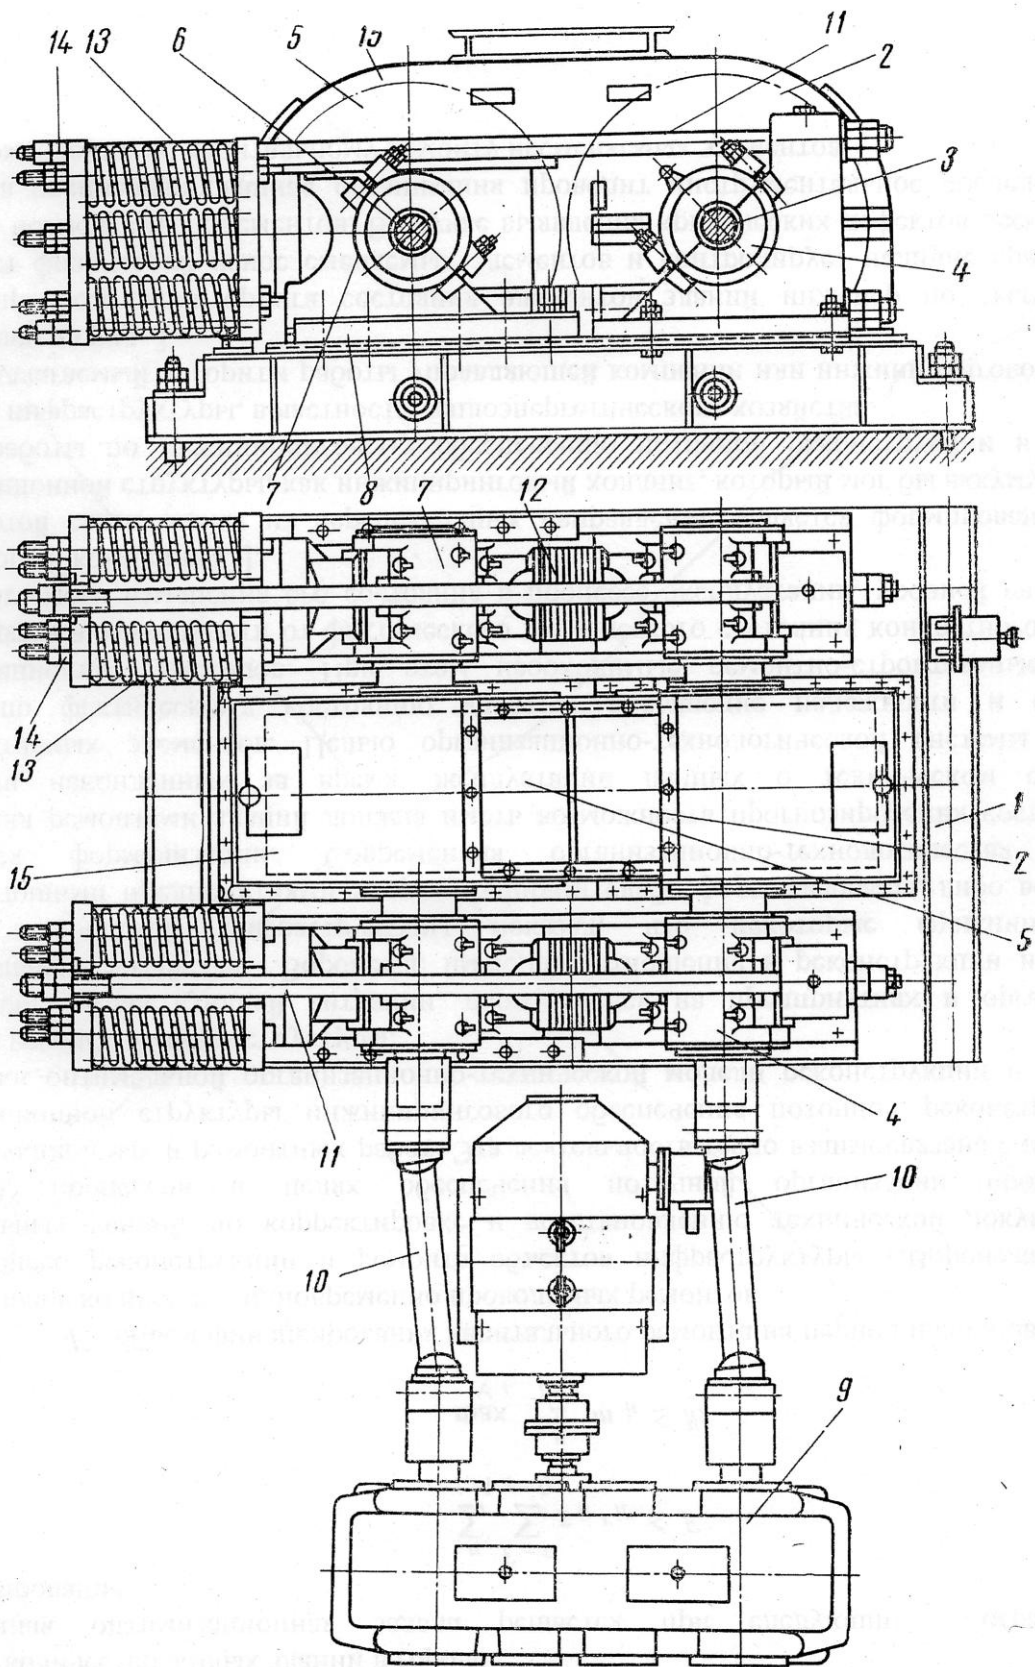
Валковая дробилка с гладкими валками: 1 – станина; 2 – валки; 3 – вал с насаженным правым валком 2; 4 – подшипники неподвижные; 5 – подвижный левый валок; 6 – вал; 7 – подшипники подвижные; 8 – направляющие для подвижных подшипников; 9 – редуктор; 10 – карданные валы; 11 – тяги; 12 – прокладки; 13 – пружины; 14 – затяжные гайки; 15 – кожух.
